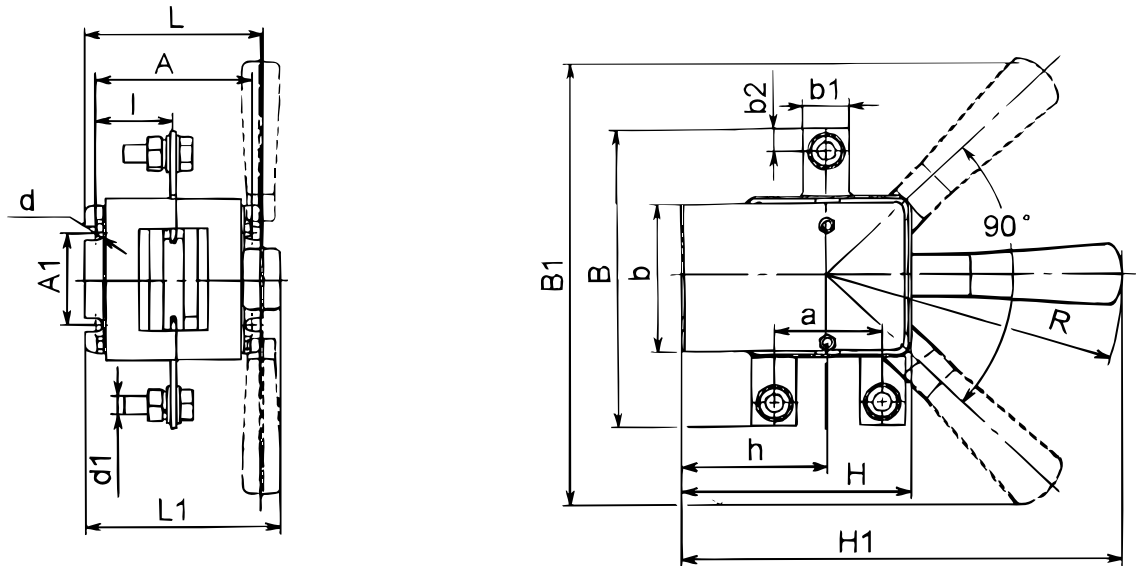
Выключатель-разъединитель однополюсный на два направления с боковой рукояткой
